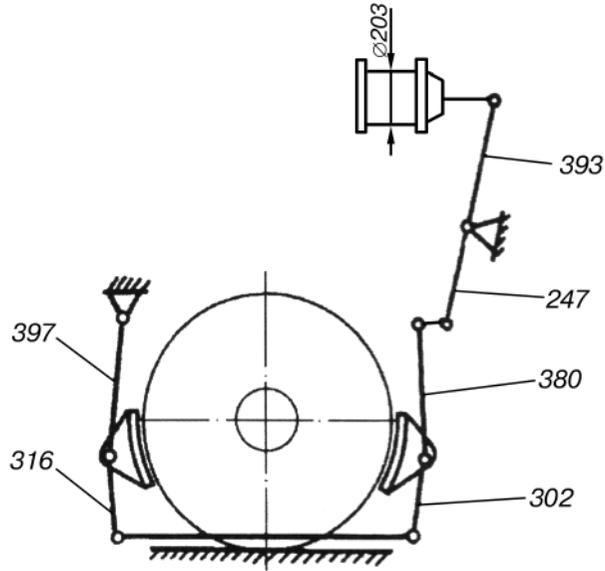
Схема рычажной тормозной передачи на одно колесо тепловоза 2ТЭ116
